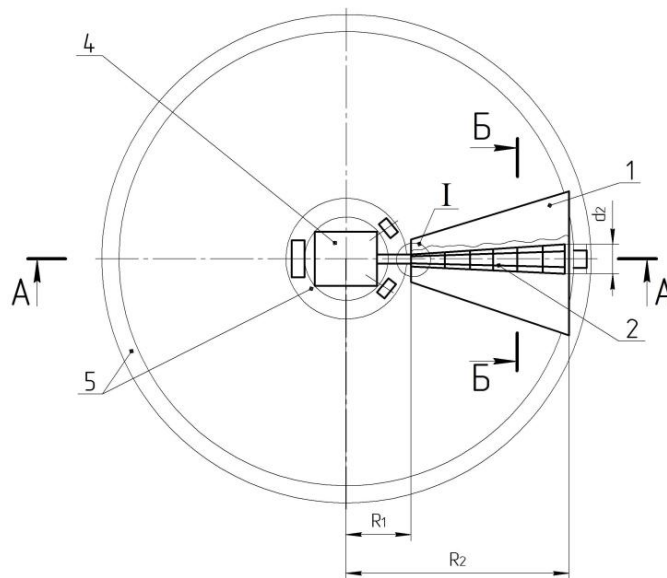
Вид сверху на пресс-форму и устройство для укладки абразивной смеси: 1-бункер; 2-барабан; 4-привод; 5-направляющие
